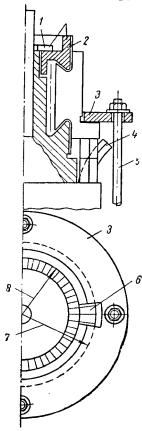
Приспособление для замены неисправных пластин коллектора:
